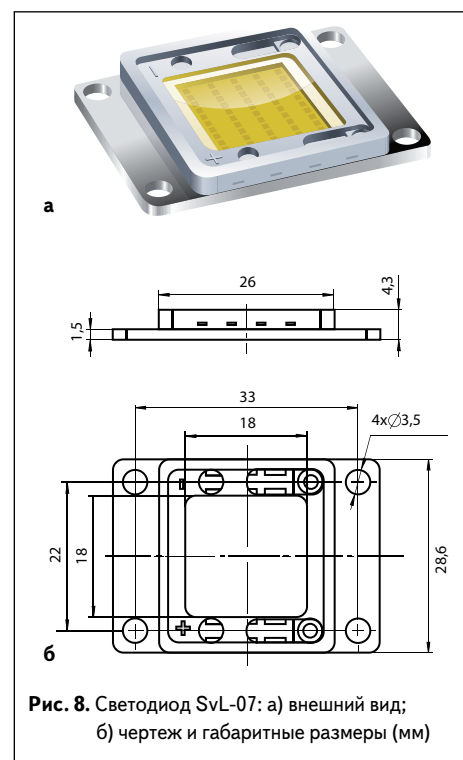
Светодиод SvL-07: а) внешний вид; б) чертеж и габаритные размеры (мм)
